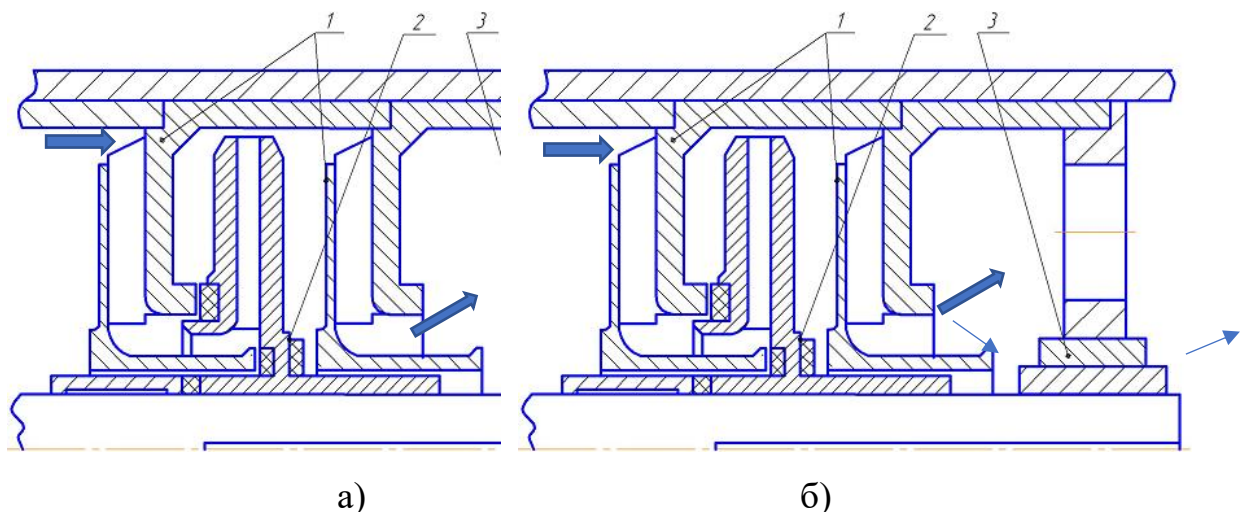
Схема испытательного узла стенда для испытаний ступеней и подшипников на износ: 1-направляющие аппараты, 2-рабочее колесо, 3-испытуемый подшипник скольжения.
